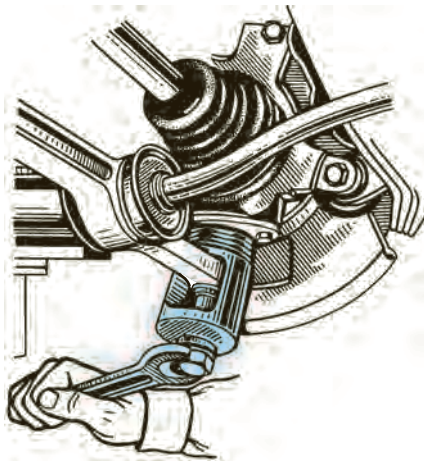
Выпрессовка конуса пальца шарового шарнира из рычага подвески
